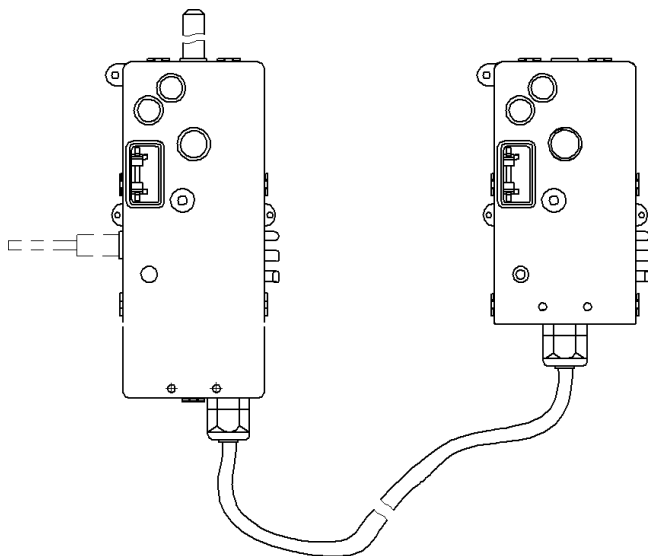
Общий вид счетчиков в корпусе Тип II
